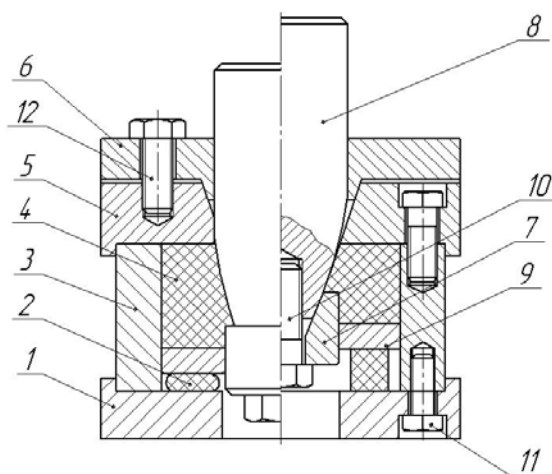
Общий вид штампа: 1 – плита штампа; 2 – эластичный буфер; 3 – контейнер; 4 – эластичный элемент; 5 – матрица; 6 – прижим; 7 – выталкиватель; 8 – пуансон; 9 – подкладная плита; 10 – болт; 11 – винт; 12 – болт
